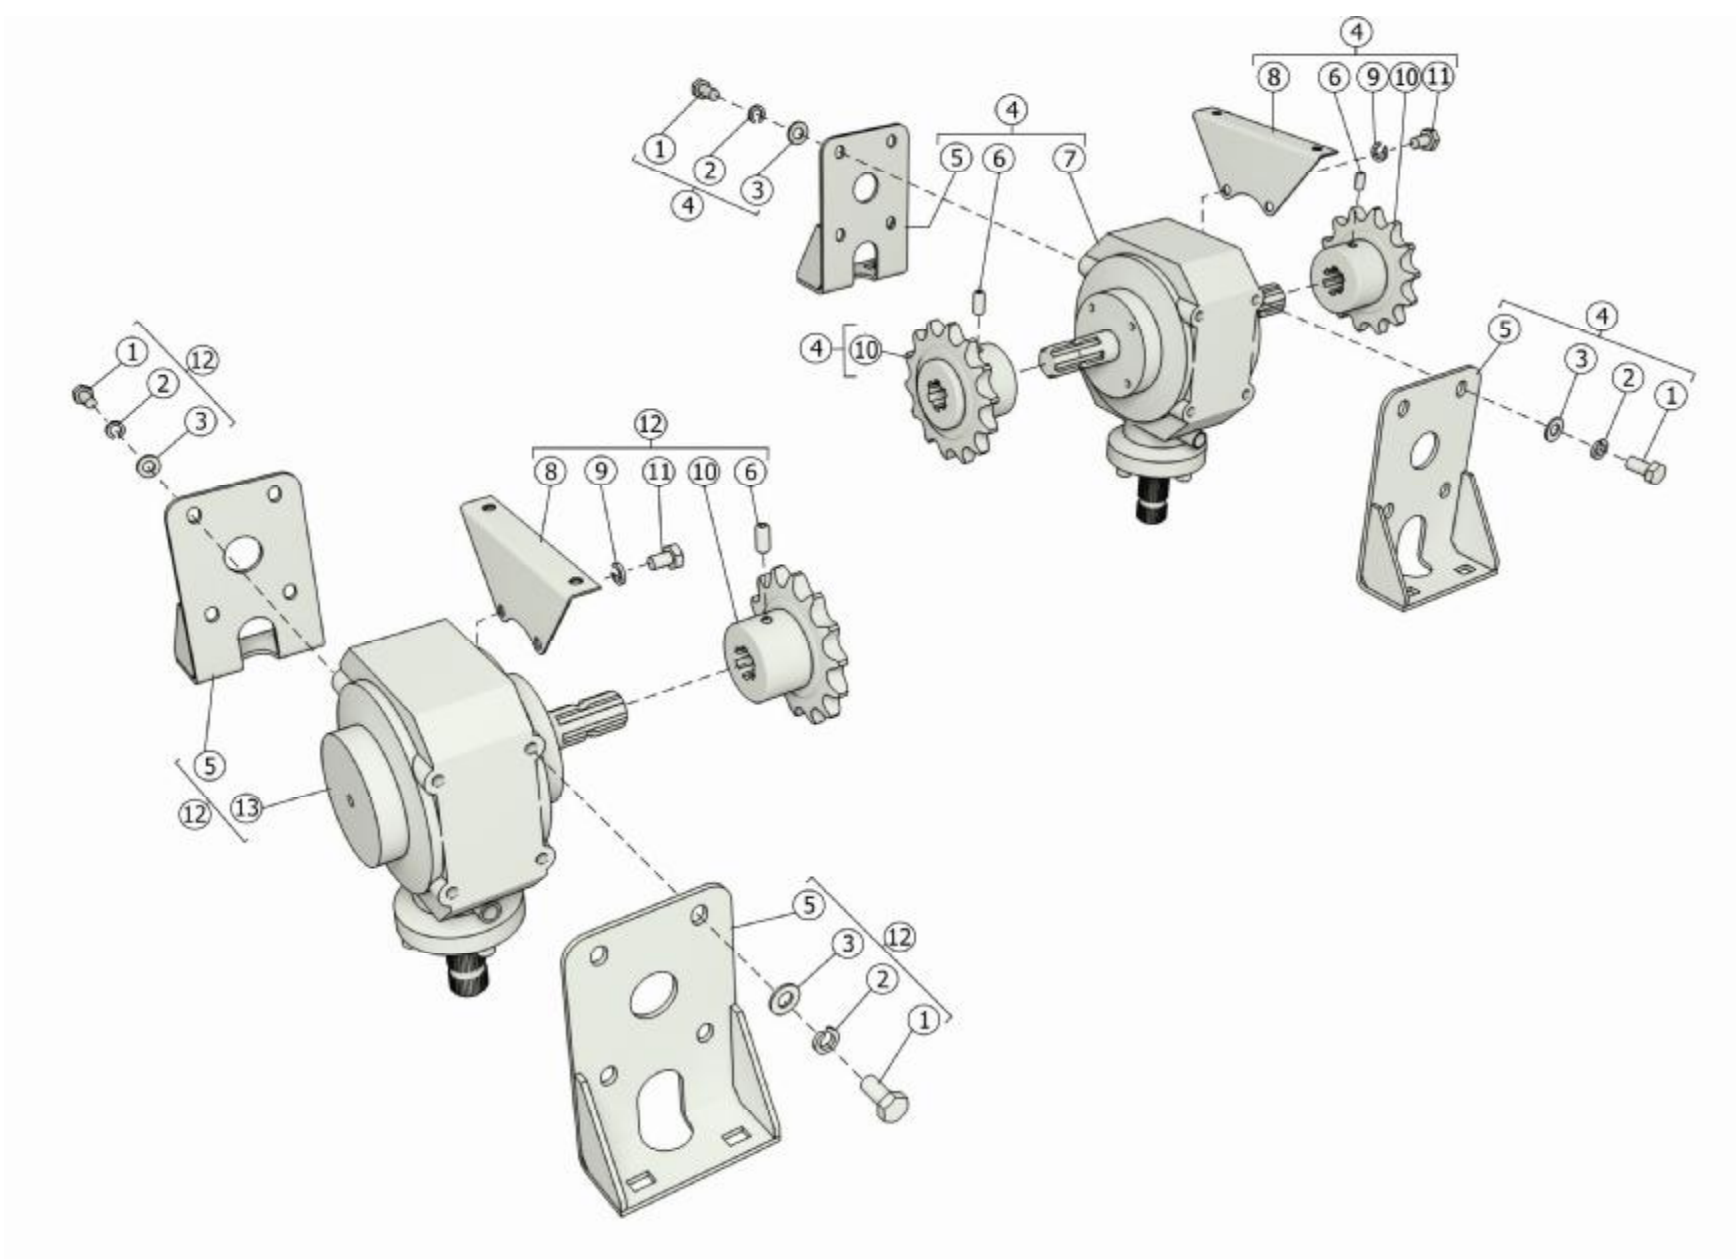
Редуктор в сборе ЖРН-601.03.02.000В. Редуктор в сборе ЖРН-601.03.02.000В-01
